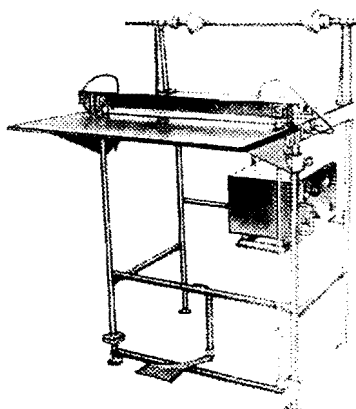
Машина марки М6-АП-2С для сварки полимерных пленок
